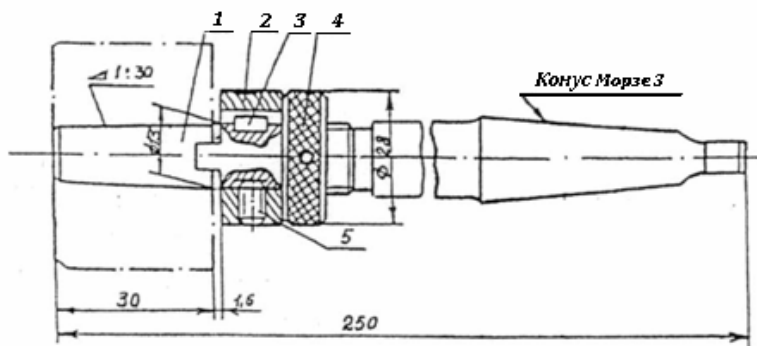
Оправка: 1 – корпус; 2 – поводок; 3 – шпонка (ГОСТ 23360-78);
